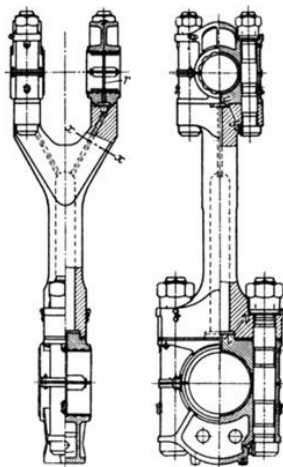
r* Ringnut für Schmierölzuführung zum Kreuzkopfbolzen und zur Gleitbahn.
